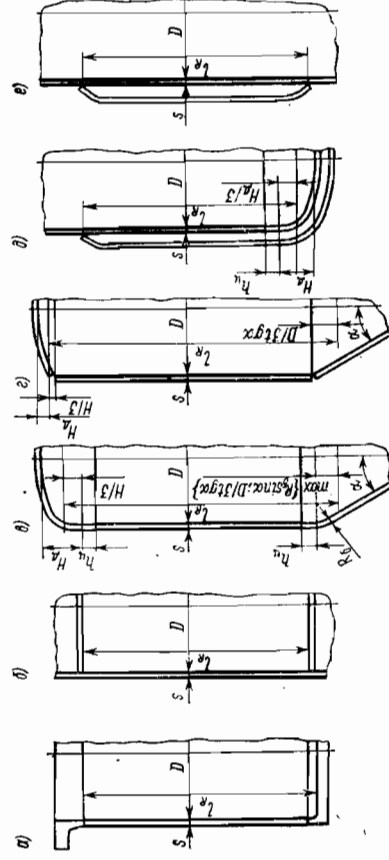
Конструкции гладких цилиндрических обечаек (корпусов) аппаратов: а — с фланцем и плоским днищем; б — с жесткими внутренними перегородками; в — с отбортованными эллиптическим и коническим днищами; г — с неотбортованными сферическим и коническим днищами; д — с рубашкой на нижней части аппарата; е — с рубашкой на средней части аппарата
